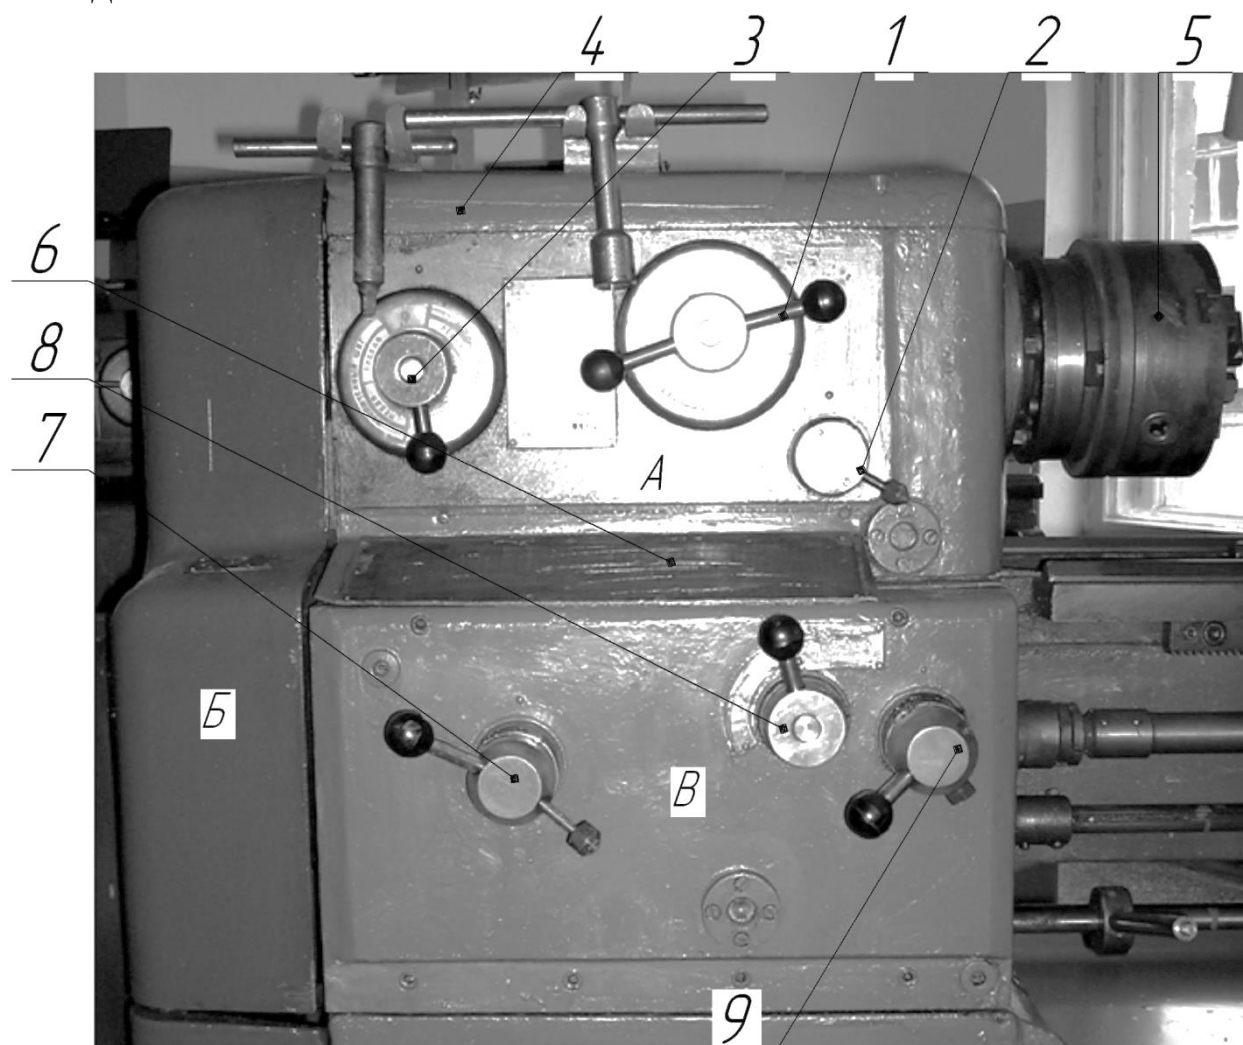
Общий вид передней бабки: А – передняя бабка с коробкой скоростей; Б – гитара; В – коробка подач; 1,2 – рукоятки переключения частоты вращения шпинделя; 3 – рукоятка реверсирования ходового винта и установка шага резьбы; 4 – крышка; 5 – трехлачковый самоцентрирующий патрон; 6 – таблица подач; 7,8 – рукоятки установки величины подач или шага резьбы; 9 – рукоятка включения ходового винта и валика
